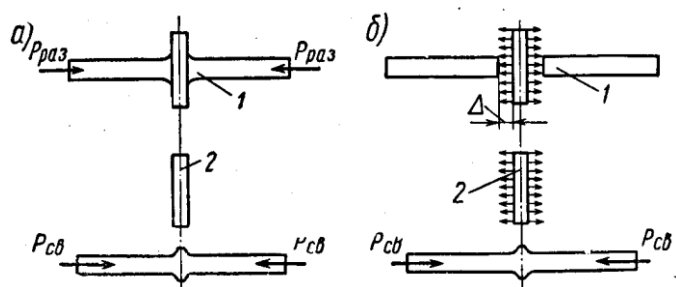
Схемы сварки при контактном разогреве (а) и излучением (б):
